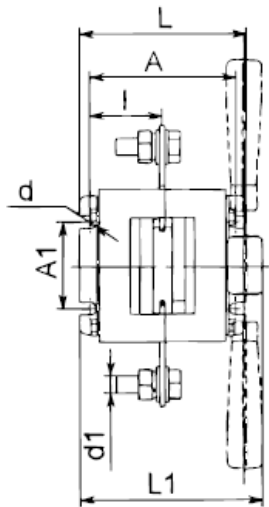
Выключатель-разъединитель однополюсный на два направления с боковой рукояткой.
